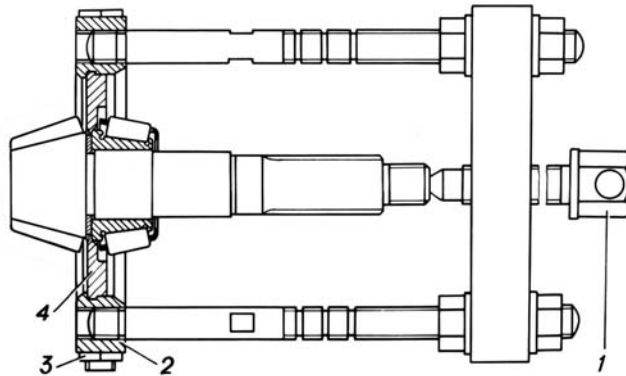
Снятие подшипника с ведущей шестерни главной передачи: 1 – винт съемника; 2 – опора; 3 – гайка; 4 – вкладыш
